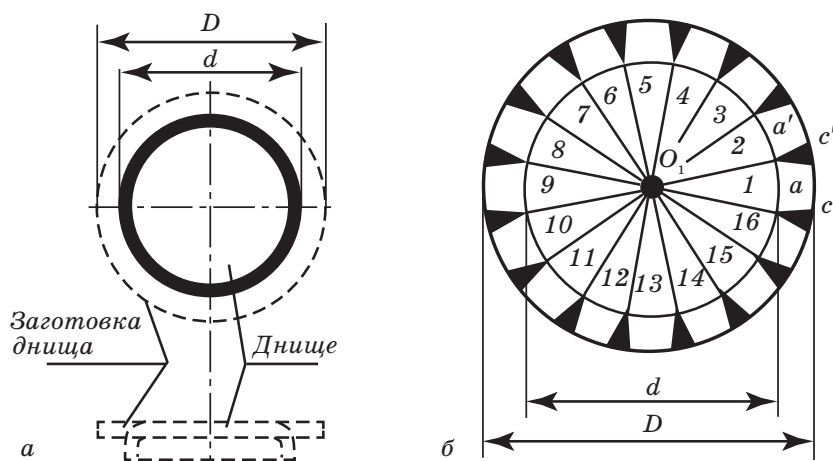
Схема посадки металу під час виготовлення деталей:
